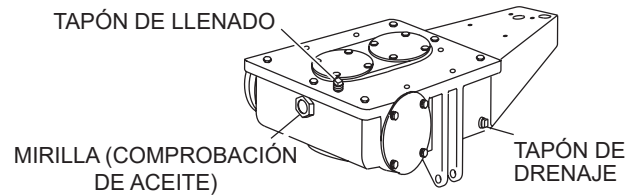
Tapones de aceite de las cajas de engranajes/Mirilla
